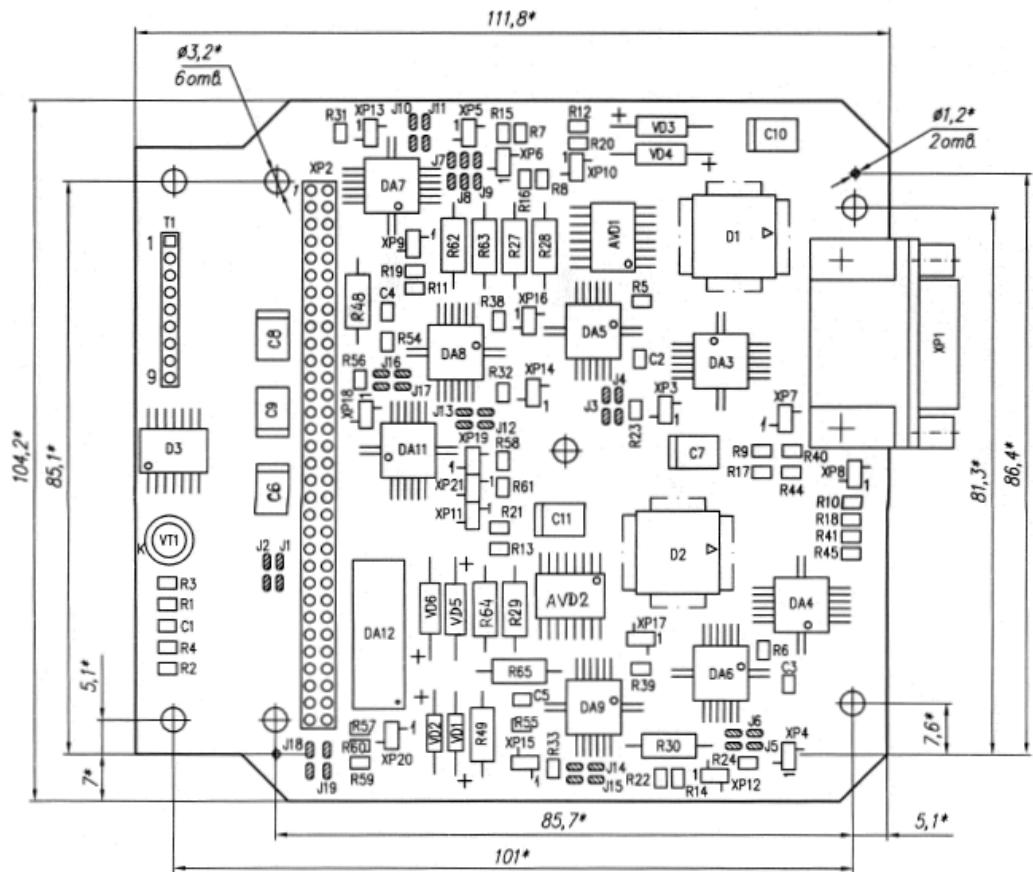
Фрагмент сборочного чертежа ячейки АМГА
